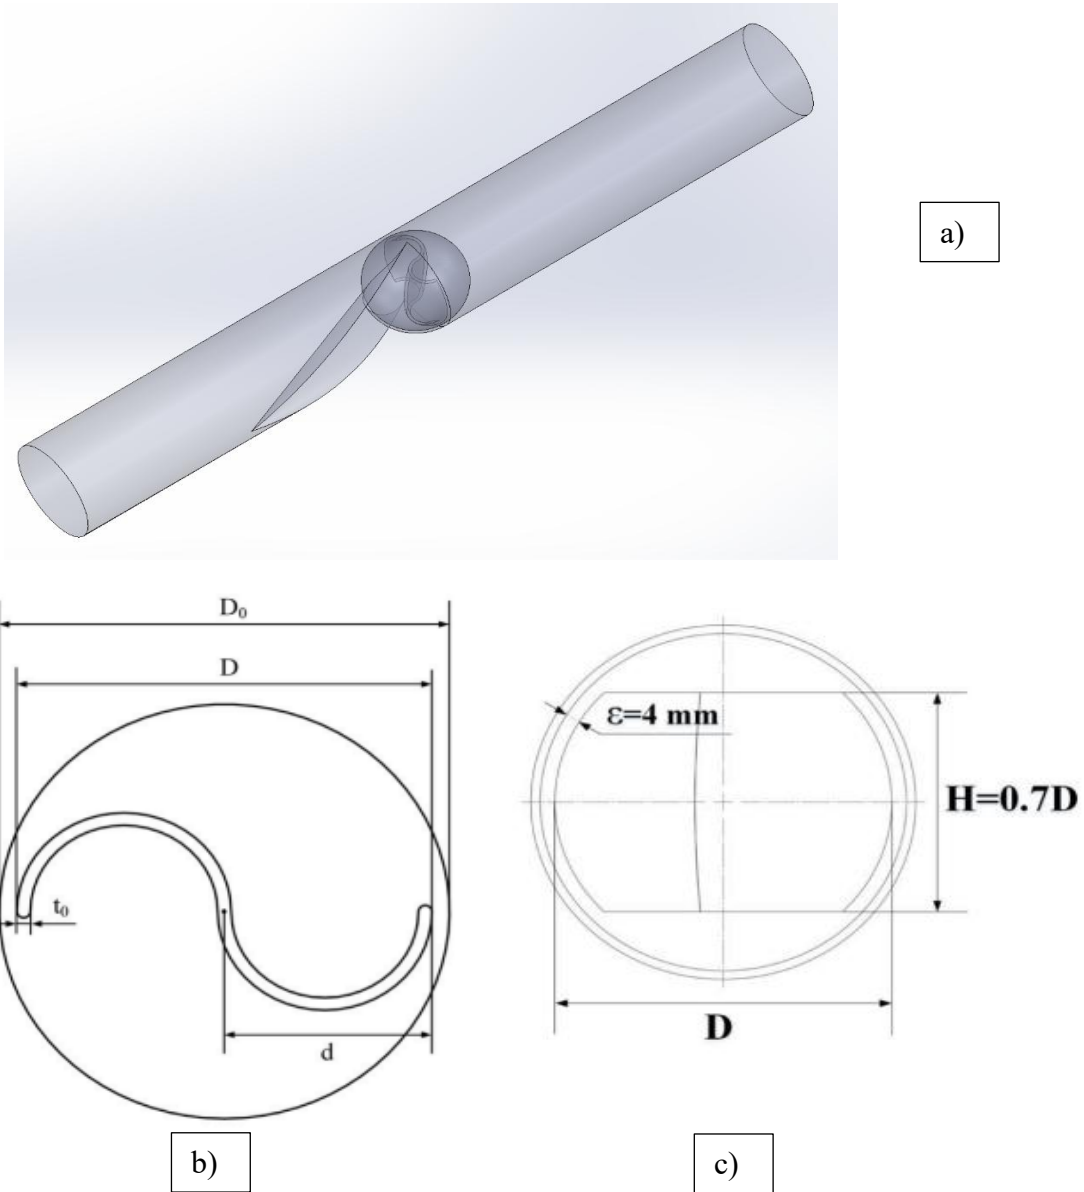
Ensamble de diseño a), turbina vista superior b) y vista frontal c).
